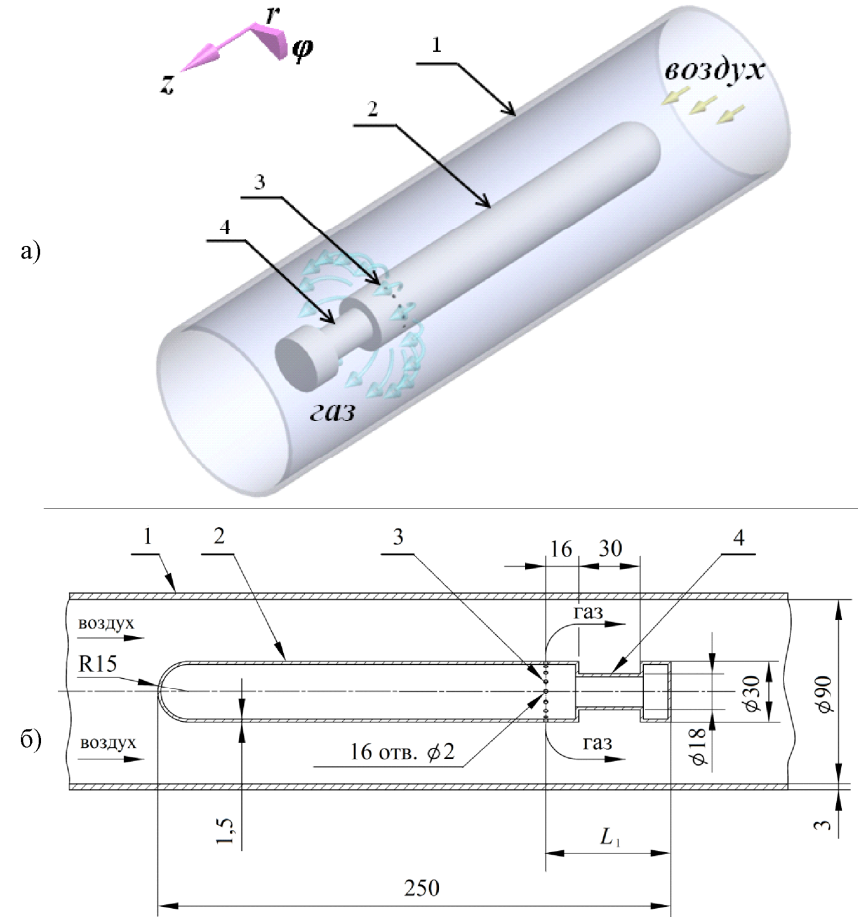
Схема (а) и продольный разрез (б) горелочного устройства с цилиндрическим стабилизатором пламени при наличии кольцевой ниши: 1) цилиндрический канал; 2) цилиндрический стабилизатор пламени; 3) газоподводящие отверстия; 4) кольцевая ниша
